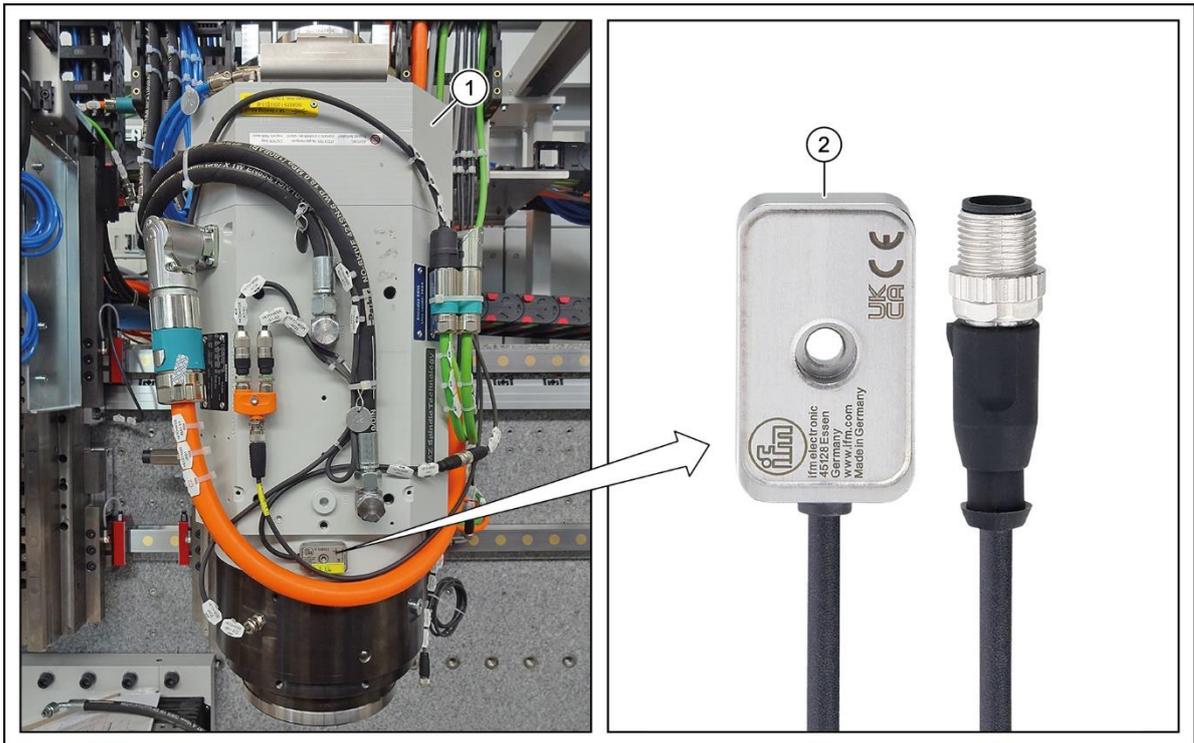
Schwingungssensor an den Werkstückspindeln - SynchroForm
